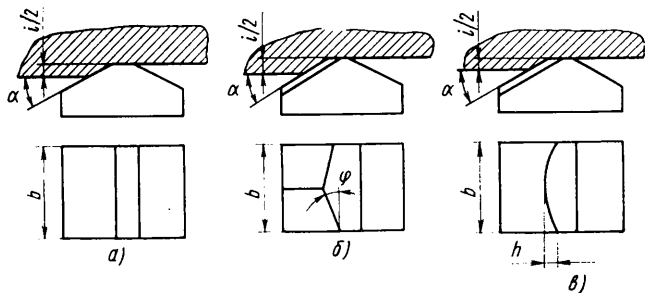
Схемы обработки дорнами с различной формой заточки заборной части: а — в виде конуса; б — цилиндрическая; в — сферическая
